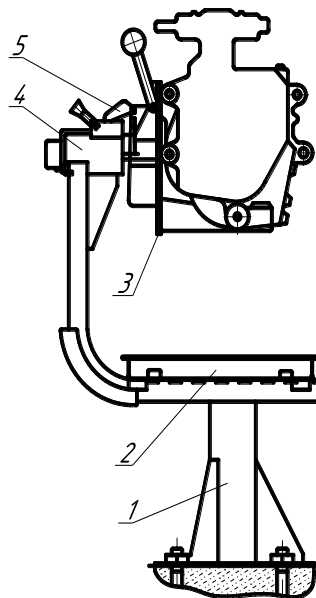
Стенд моделі ПР 77: 1 – стійка; 2 – піддон; 3 – стіл поворотний; 4 – корпус підшипників; 5 – стопор [2].
